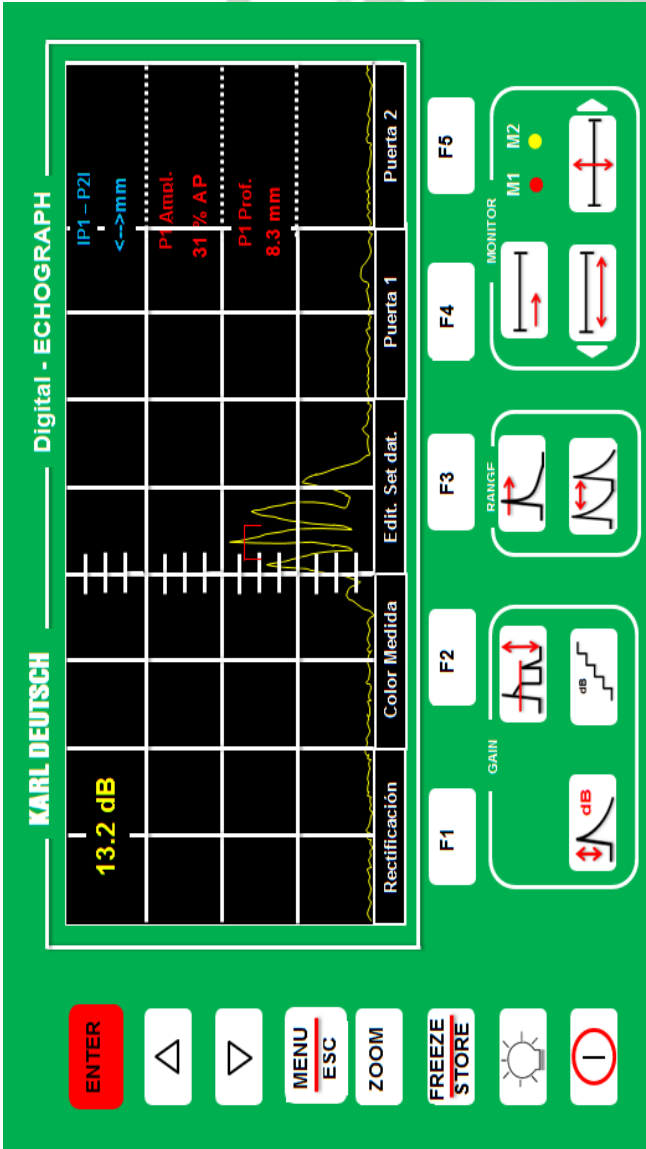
Pantalla de Inspección 2 lado izquierdo
